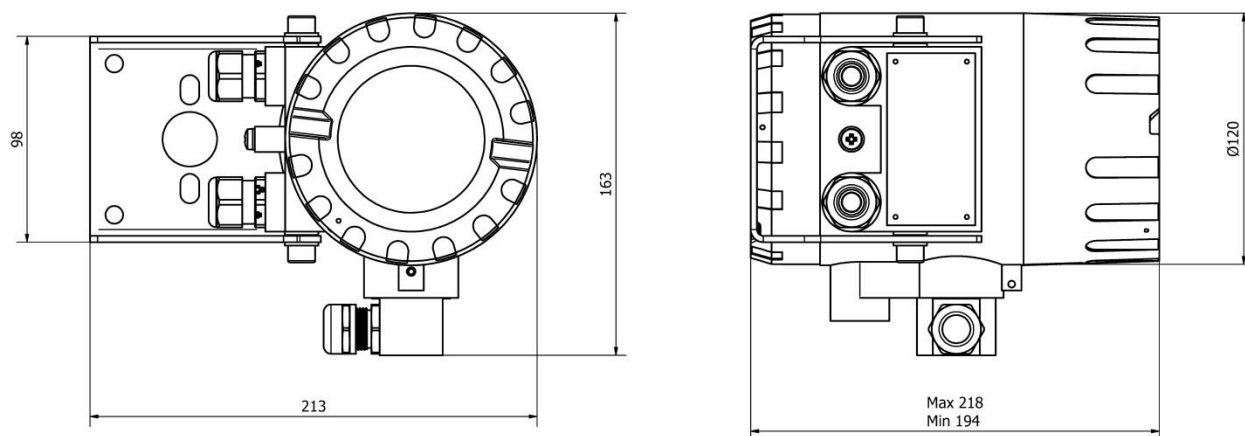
Индикатор расходомера с креплением. Габаритные размеры
